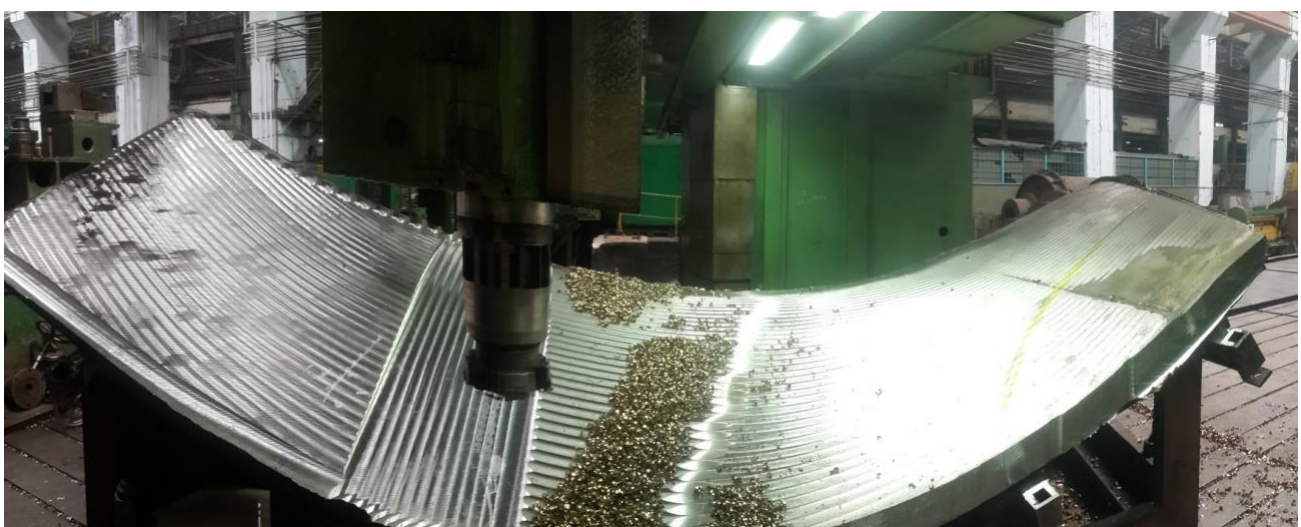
Приспособление для фрезерования «тыльной» стороны лопасти
